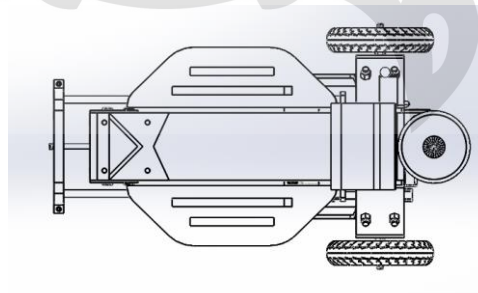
Diseño del soporte o chasis de la cortadora hidráulica
